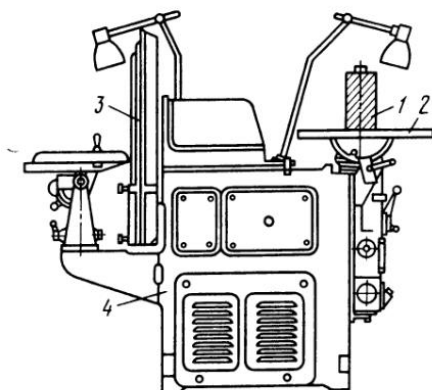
Дисковый шлифовальный станок ШЛДБ-3:
